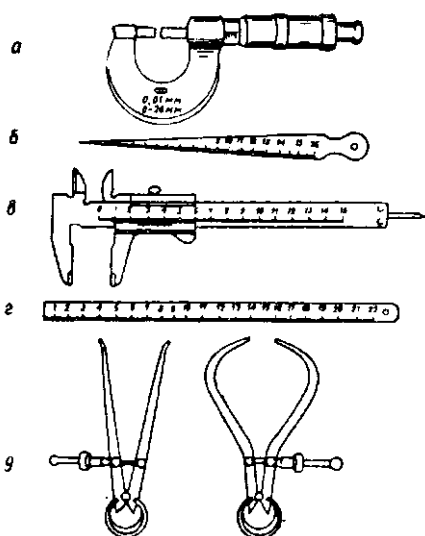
Измерительные инструменты: а — микрометр; б — нутромер; в — штангенциркуль; г — измерительная линейка; д — кронциркули.
